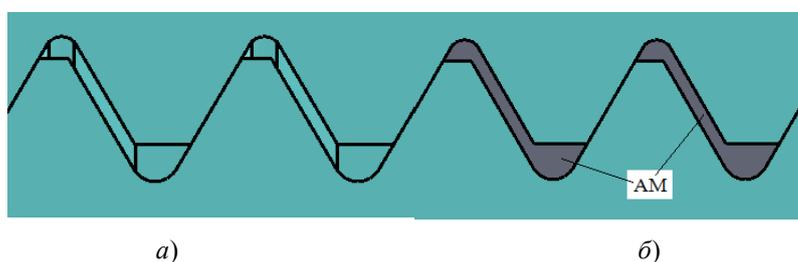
Варианты сборки резьбовых соединений типа стяжки:
